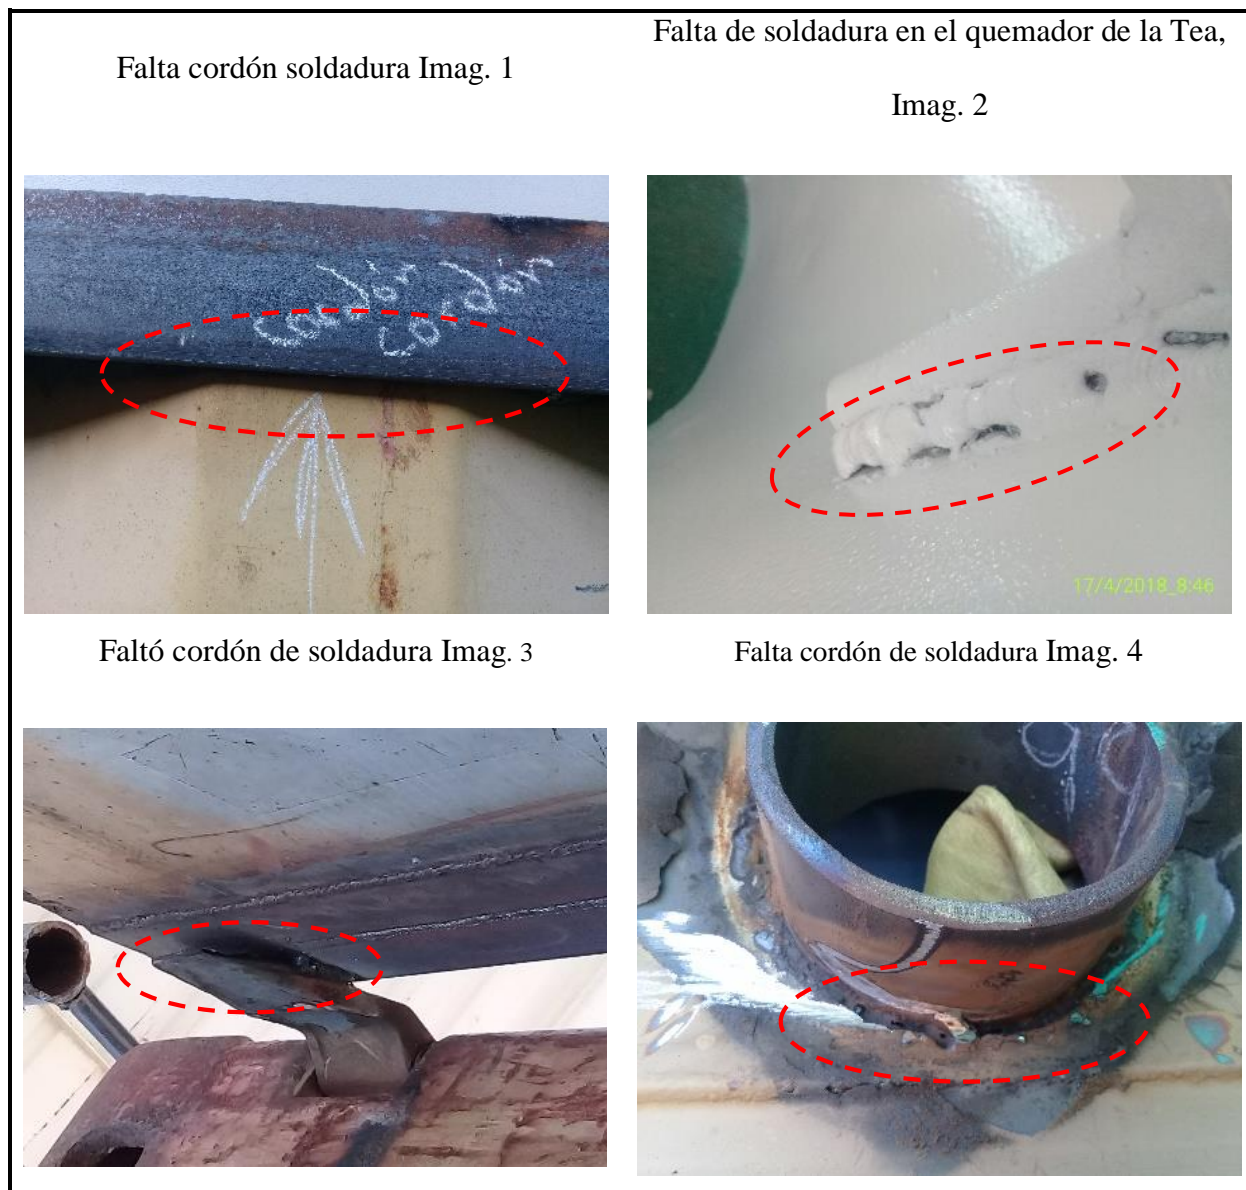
Inspección en el área de soldadura. (1 parte)
